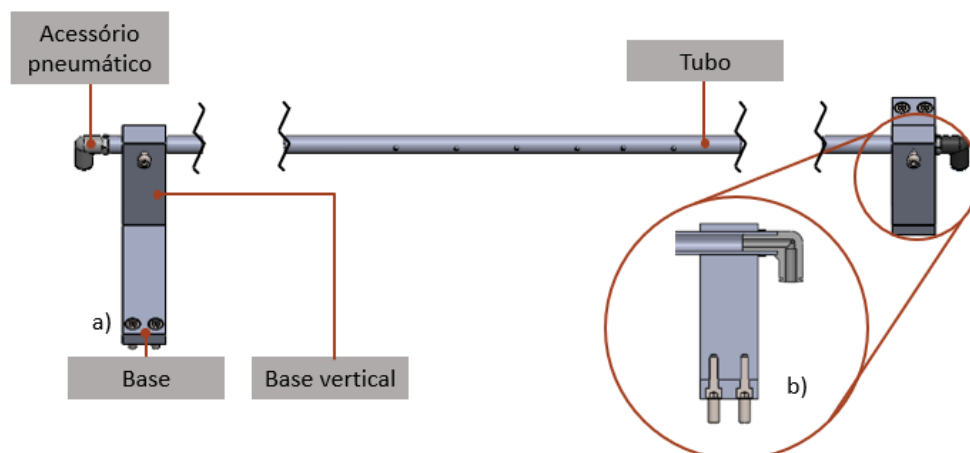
Kit* de sopro IBK2 L1: a) vista geral; b) vista em corte
